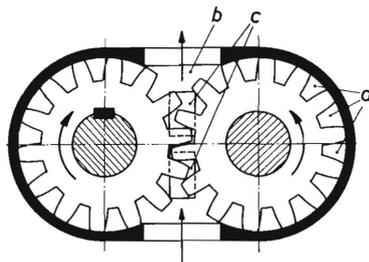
Schema einer Zahnradpumpe. Doppelläufersystem.
